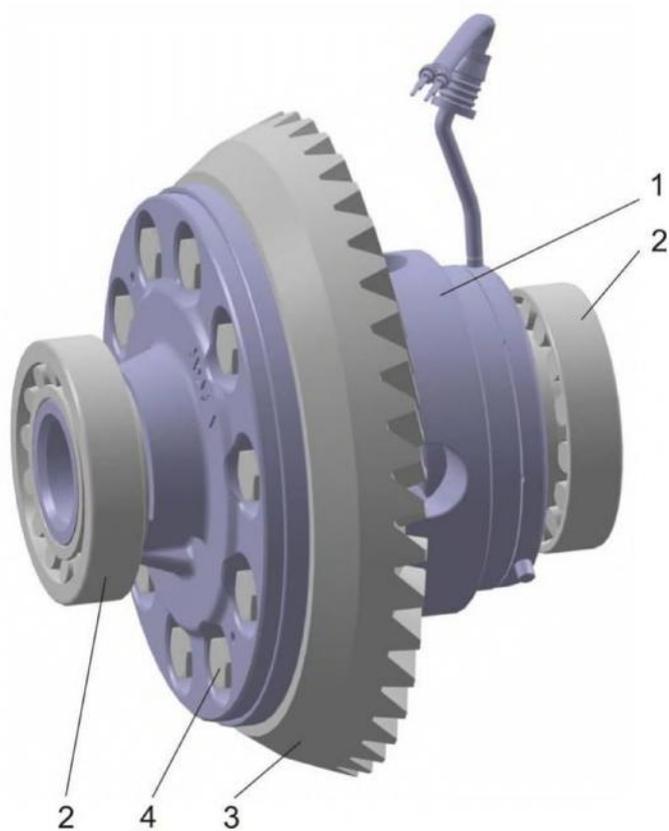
Блокируемый дифференциал в сборе с подшипниками и ведомой шестерней главной передачи: 1 – дифференциал; 2- подшипники; 3 – шестерня ведомая; 4 – болт
